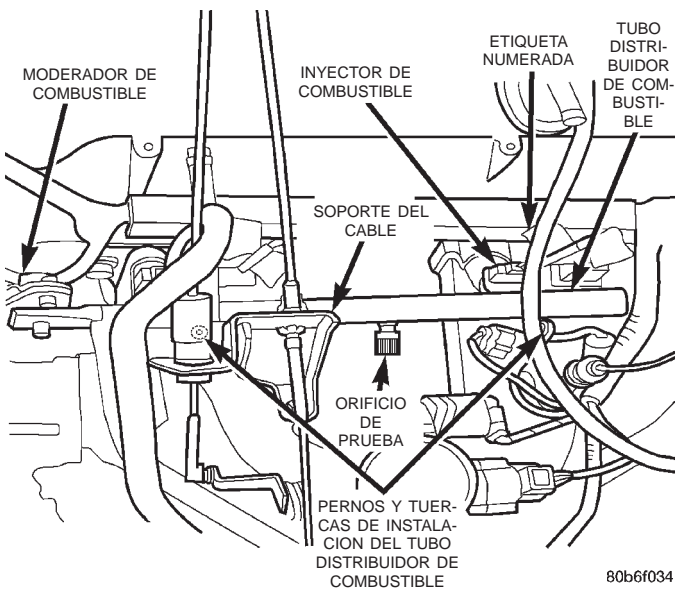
Montaje del tubo distribuidor de combustible—Motor 2.5L
